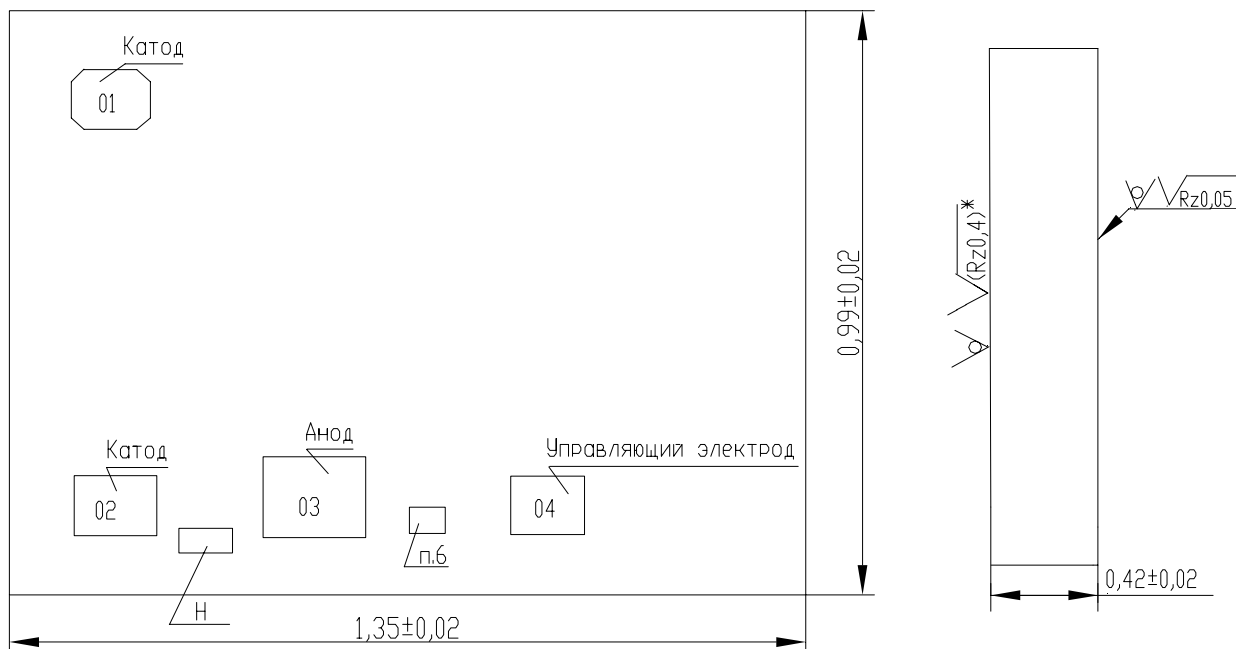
Габаритный чертеж кристалла 142EP1H4ИМ
